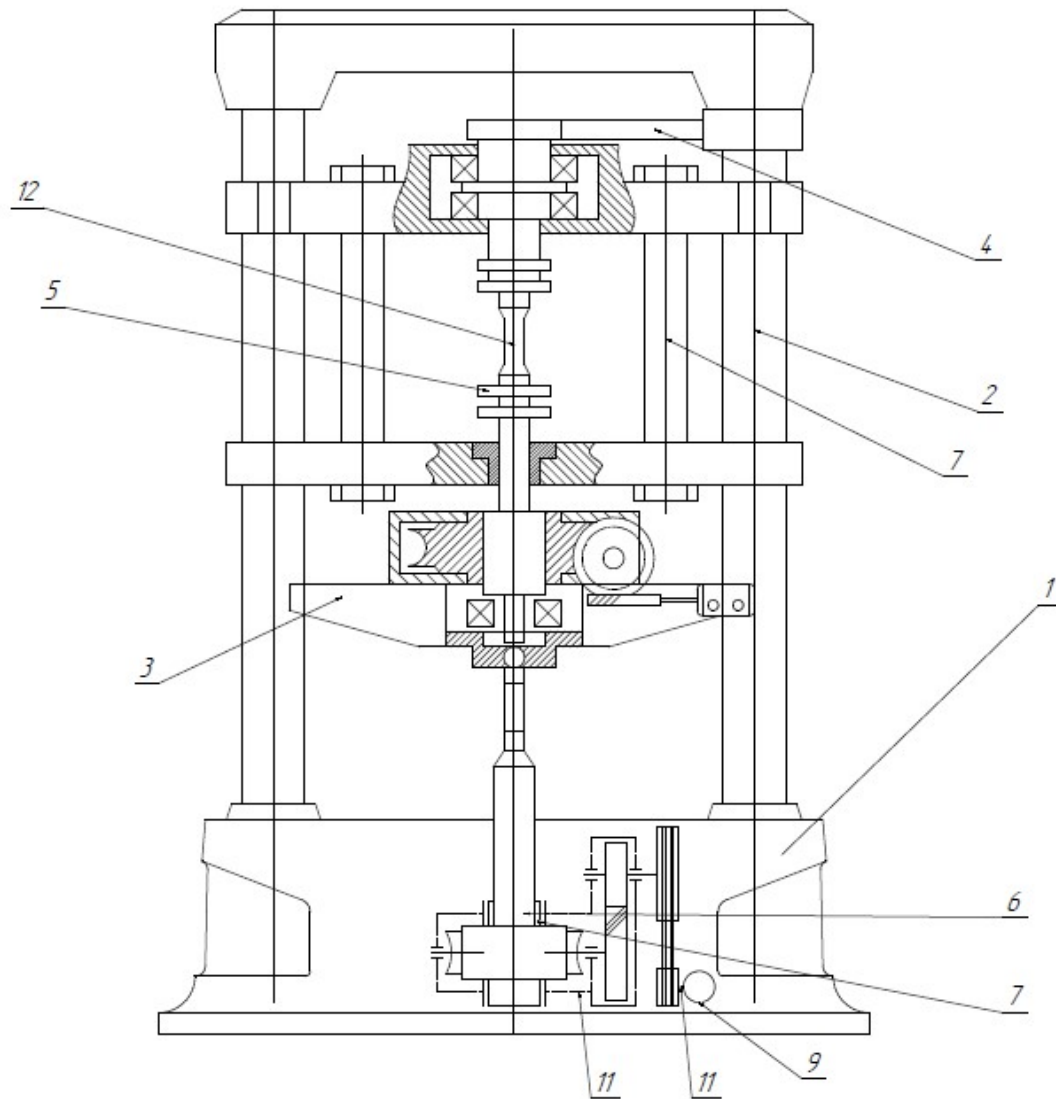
установки: 1 – основа; 2 – колона; 3 – рухома траверса; 4 – динамометр; 5 – нижній захват; 6-гвинт; 7 – гайка с насадженням черв'яком, 9– двигун, 10- жорстка муфта 11- редуктор, 12-зразок, 13-нерухомий хват верхній, 14-стіл, 15- редуктор черв'ячний, редуктор циліндрично черв'ячний
